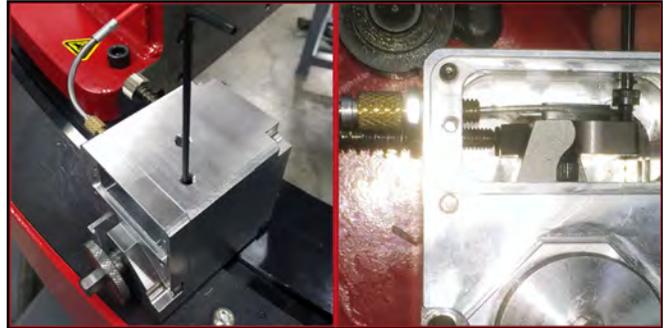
POSITION DER M4-SCHRAUBE (LINKS); KABELENDE UNTER DER M4-SCHRAUBE UND KONTERMUTTER MIT EINSTELLSCHRAUBE (RECHTS)
